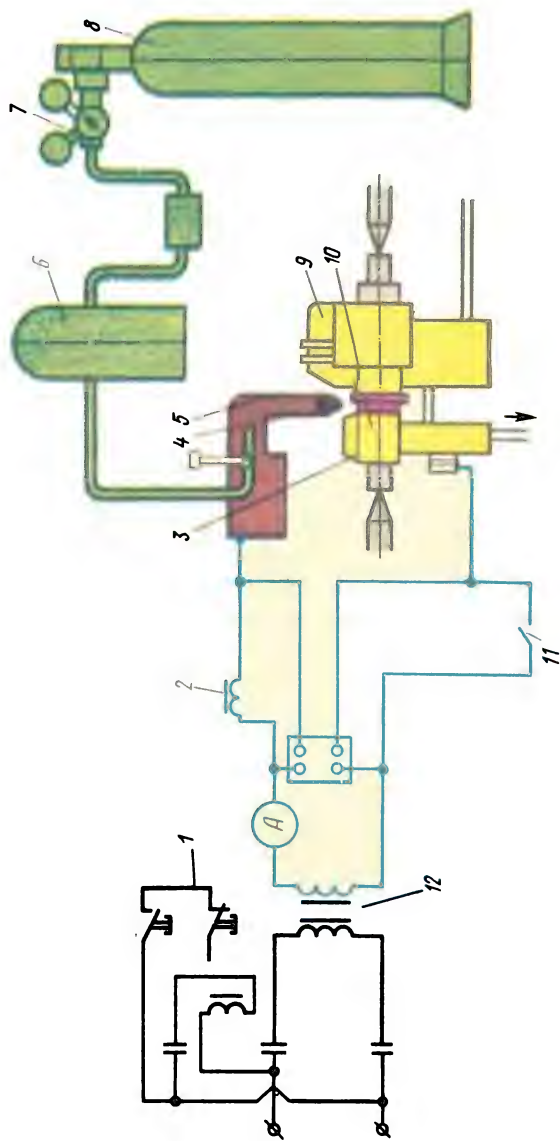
Принципиальная схема установки для аргоно-дуговой сварки концов секций с петушками кол лкторных пластин
